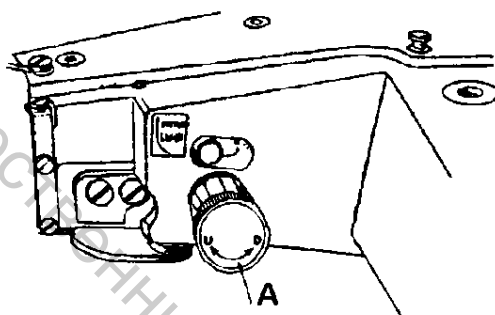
Регулировка зубчатой рейки по высоте
